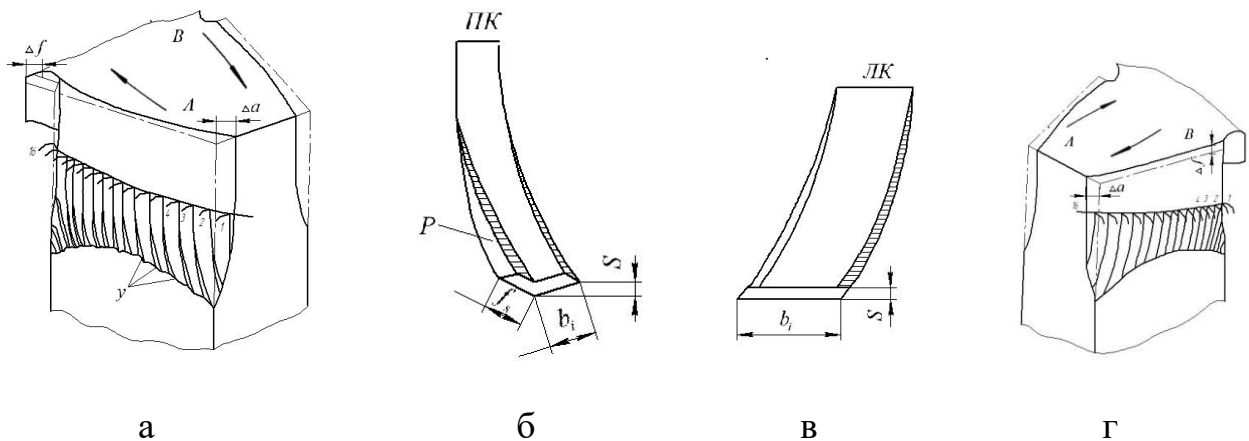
Форма шарів, зрізаних зубами правозахідної фрези з роздільною схемою формоутворення: а - утворення уступів (У) при роботі правого корпусу; б - форма шару, зрізаного зубами правого корпусу; в - форма шару, зрізаного зубами лівого корпусу; г - схема обробки поверхні зуба лівим корпусом
